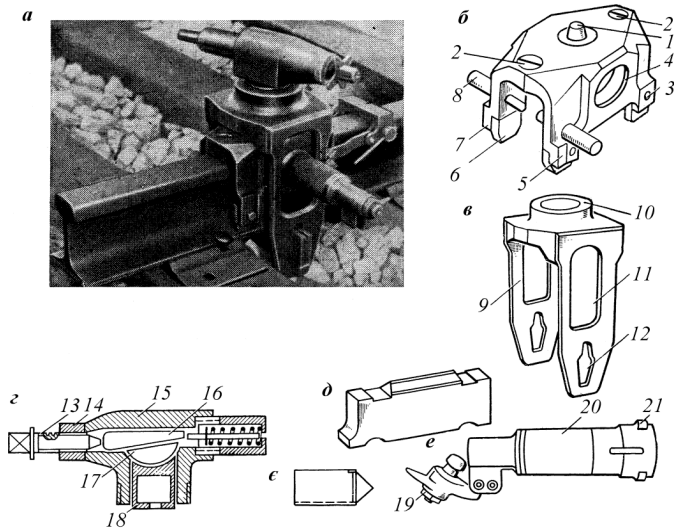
Пороховий рейкозламувач ПР-1:
